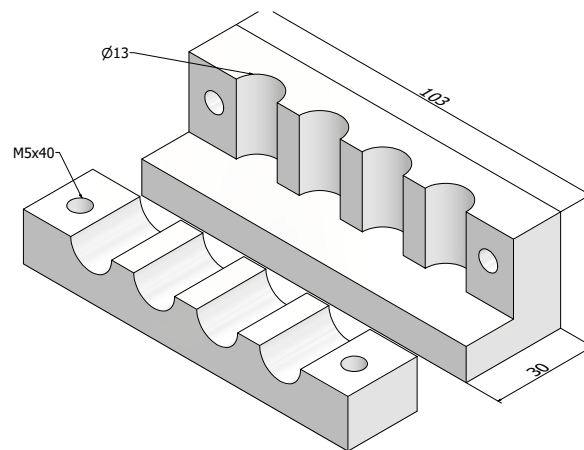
Molde probetas de cemento y sus dimensiones en [mm].
